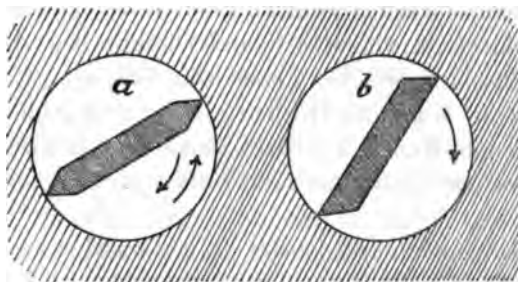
Bohren mit zweischneidigem und einschneidigem Bohrer.
